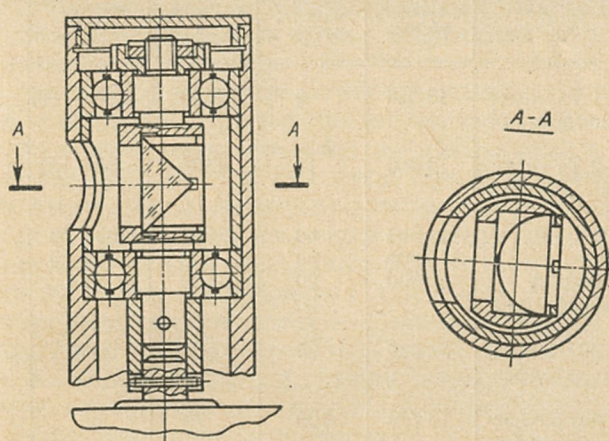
Вариант крепления вращающейся призмы с двумя опорами.
